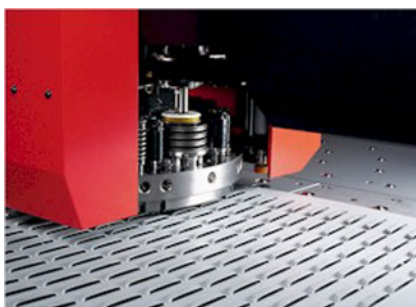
reZ) Einbringen von Kiemen mit Standardwerkzeug (Amada)
